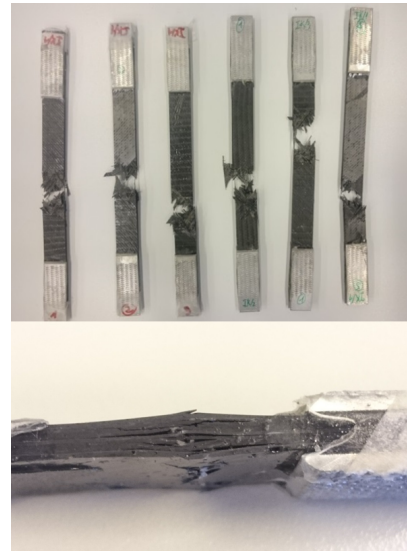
Probetas ensayadas a tracción (imagen superior) y compresión (imagen inferior).
